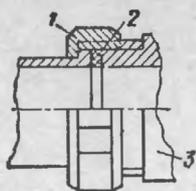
Соединение глушителя с выпускным патрубком цилиндра (сечение Д—Д по рис. 58)
